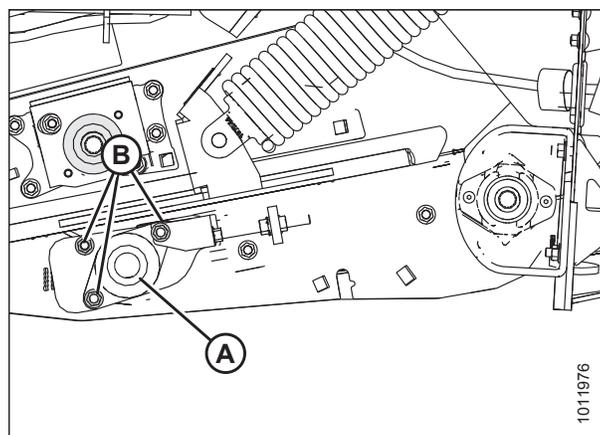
Rodillo tensor de la plataforma trasera izquierda
